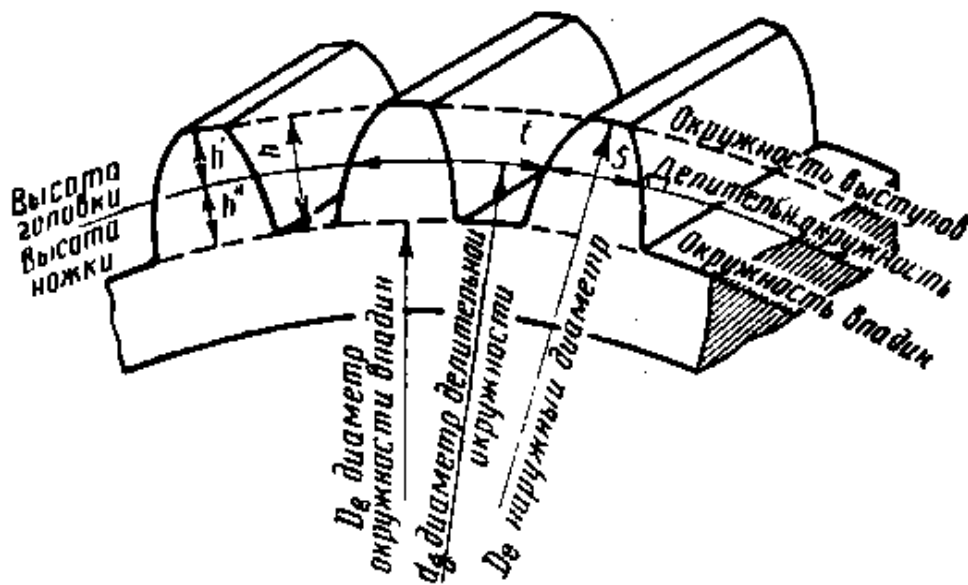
Элементы цилиндрического зубчатого колеса
